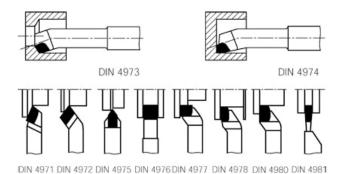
Werkzeugformen beim Drehen für verschiedene Bearbeitungsaufgaben / Geometria sculelor de strunjit cu plăcuţe din carburi metalice
